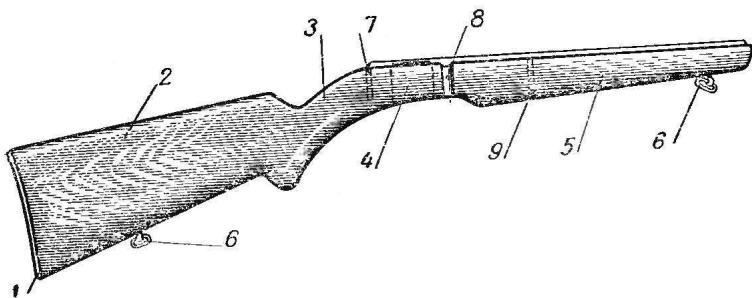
Ложа: 1 — затыльник; 2 — приклад; 3 — шейка; 4 — щель для спускового механизма; 5 — цевье; 6 — антабки; 7 — гнездо для хвостового винта; 8 — выем для рукоятки затвора; 9 — отверстие для винта упора
